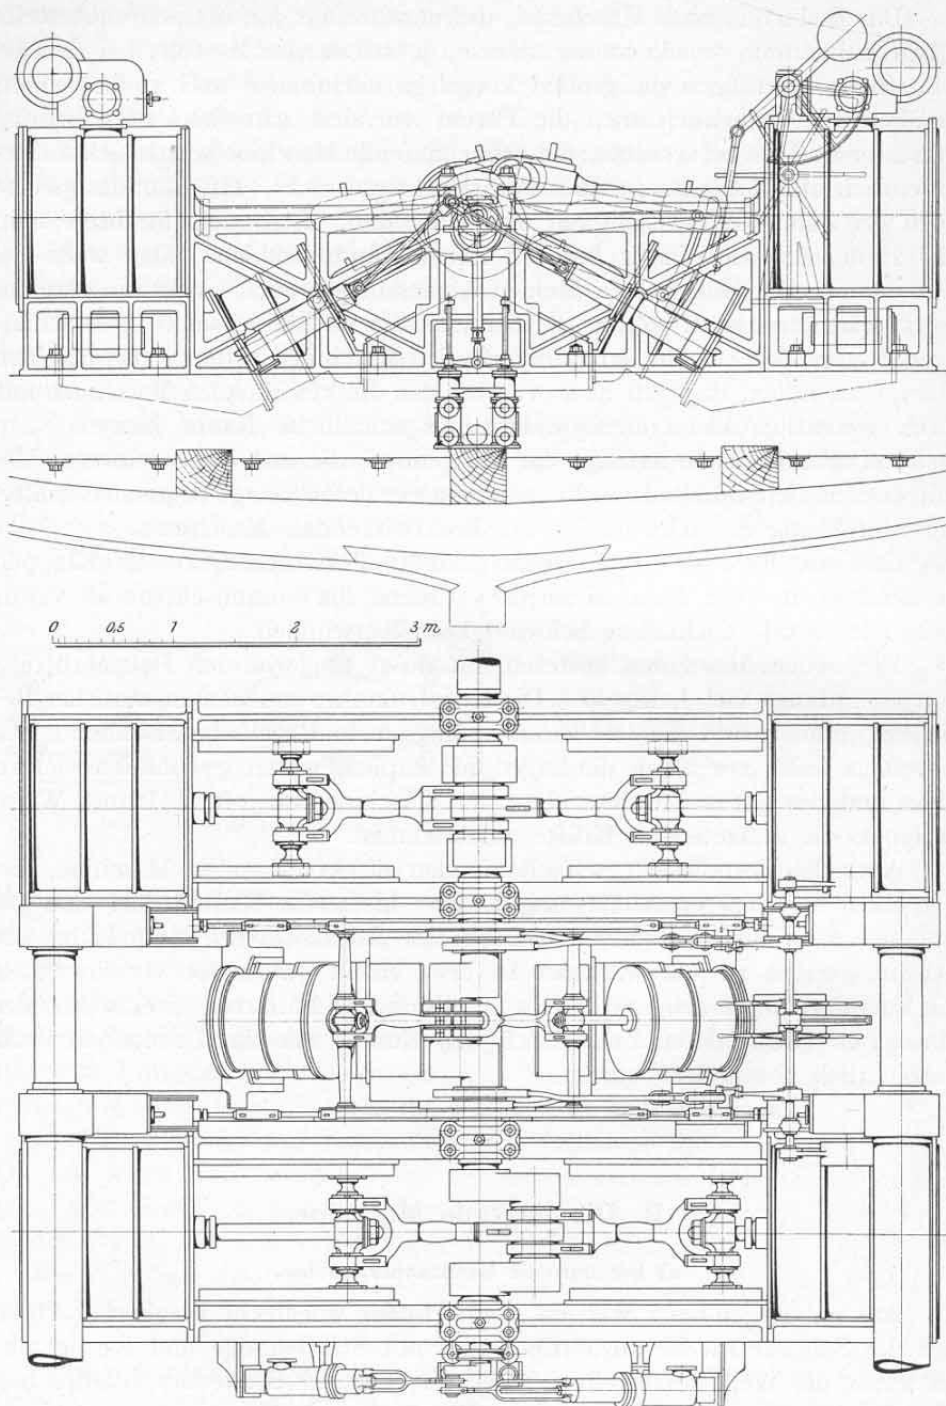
und 603. Liegende Schraubenschiffmaschine mit 4 Zylindern von Watt & Co.
